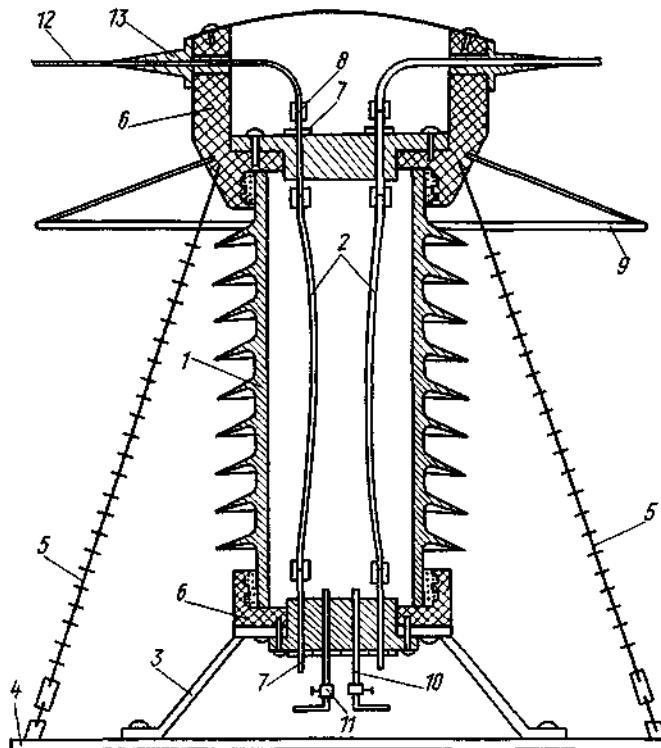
Жесткая опорная изоляционная конструкция со световодами на базе колонки полых керамических опорных изоляторов:
